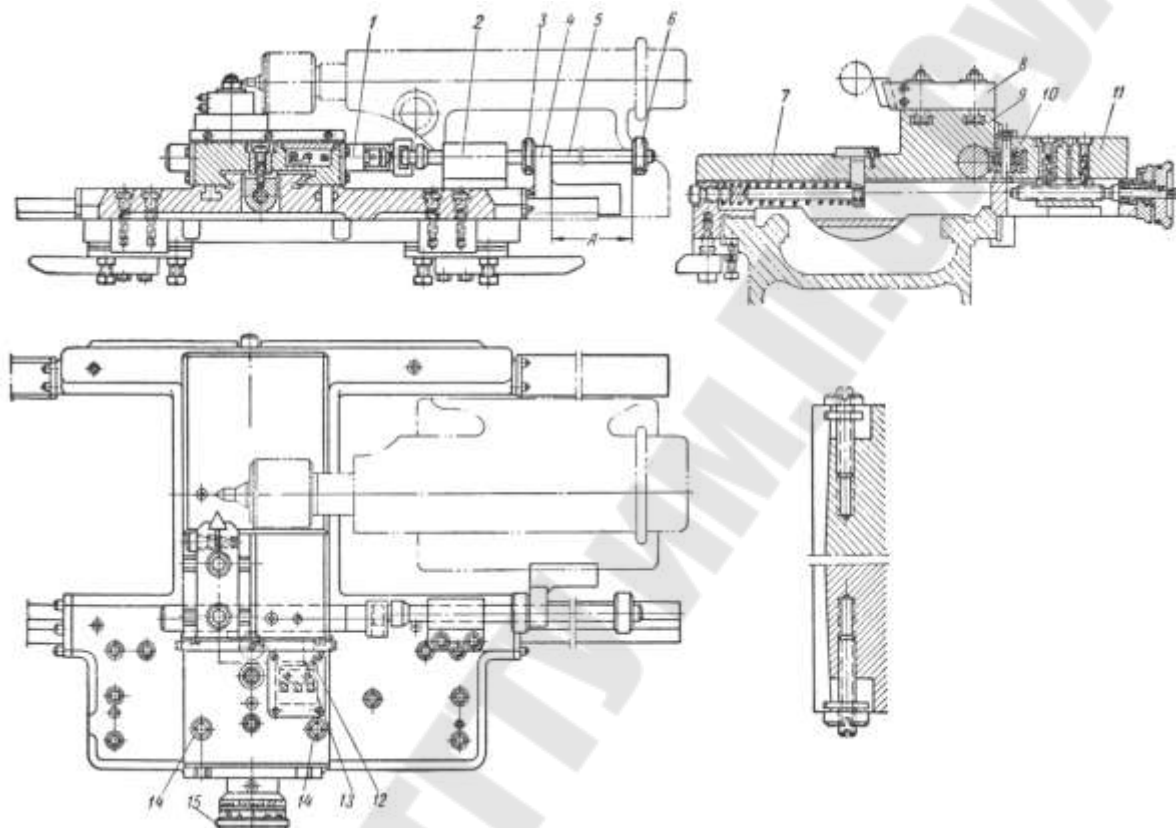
Суппорт токарного полуавтомата модели КТ-16
